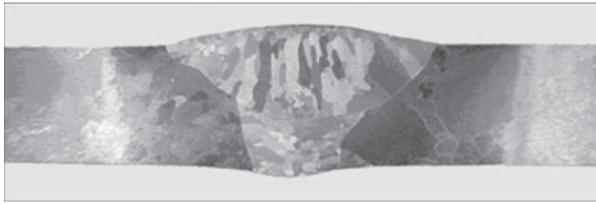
Макрошлиф сварного соединения сплава ВТ22 толщиной 8 мм (в состоянии после сварки)
